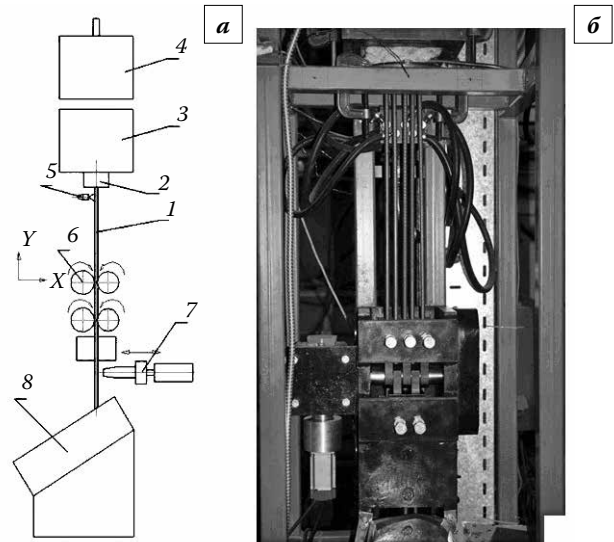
Установка непрерывного вертикального литья прутков из медно-фосфорных сплавов: а – принципиальная схема, 1 – литая заготовка; 2 – кристаллизатор; 3 – металлоприемник; 4 – дозирующий узел; 5 – форсунка вторичного охлаждения; 6 – тянущий узел; 7 – гидравлический нож; 8 – лоток для сбора прутков; б – фотография установки со стороны тянущего узла
